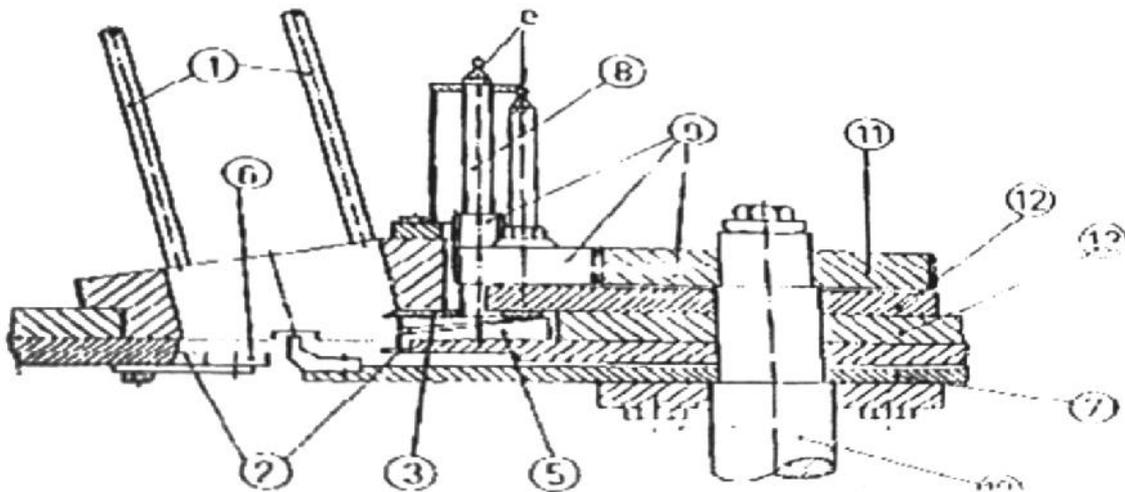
Dessin technique de l'alimentateur de couvercles
